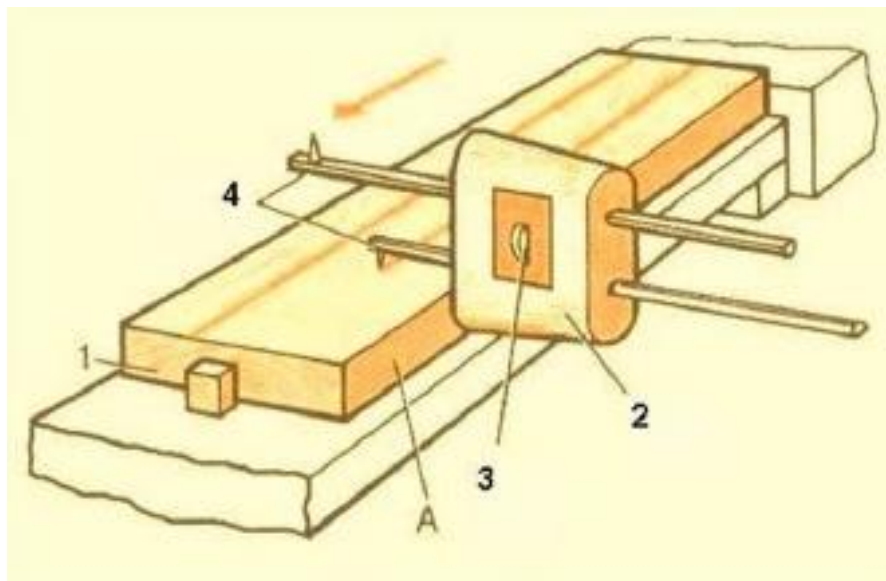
Рейсмус для розмічання: 1 – заготовка; 2 – колодка; 3 – фіксатор (клин); 4 – бруски зі шпильками. А – базова поверхня для розмічання
